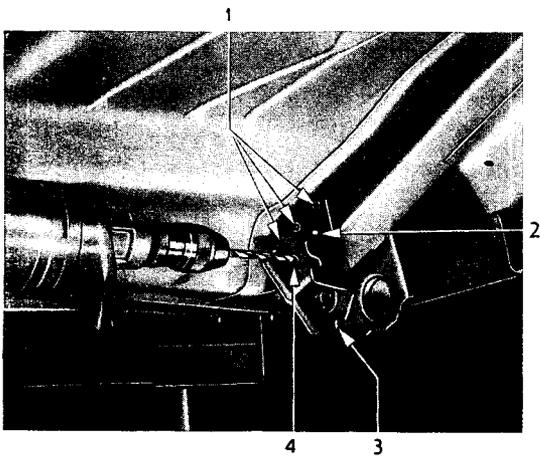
Warzenschweißpunkte an innerer Stütze ausbohren
